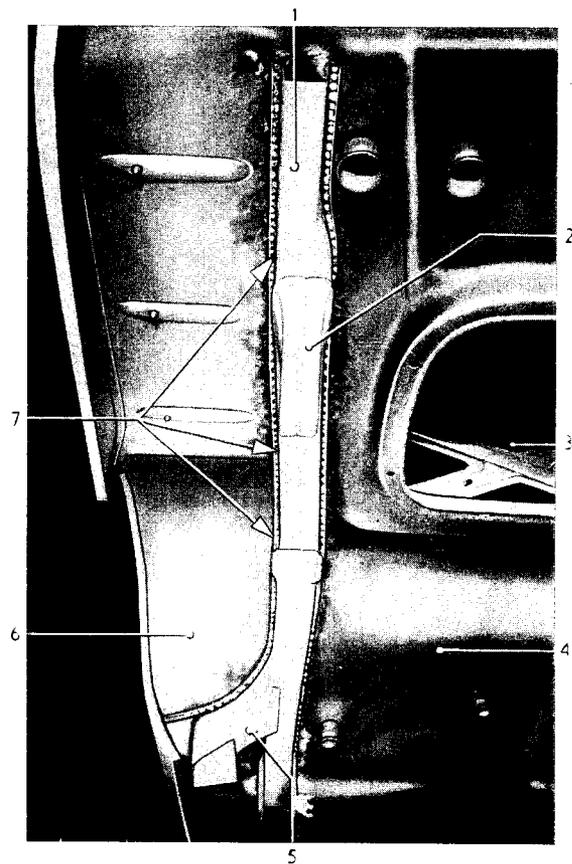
Hinterlängsträger am Bodenblech punktgeschweißt
